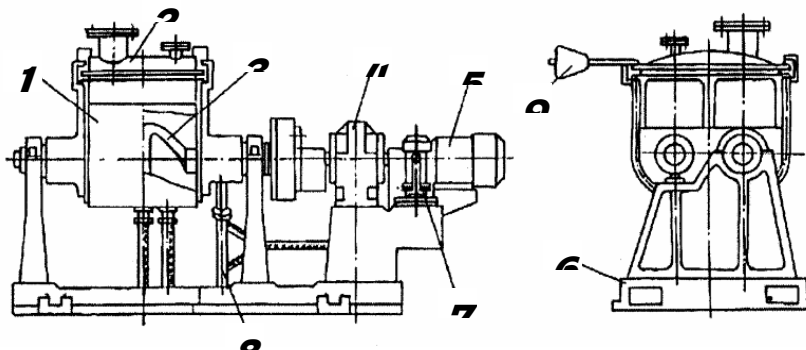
Смеситель с Z-образными лопастями ЗЛ-250-01
